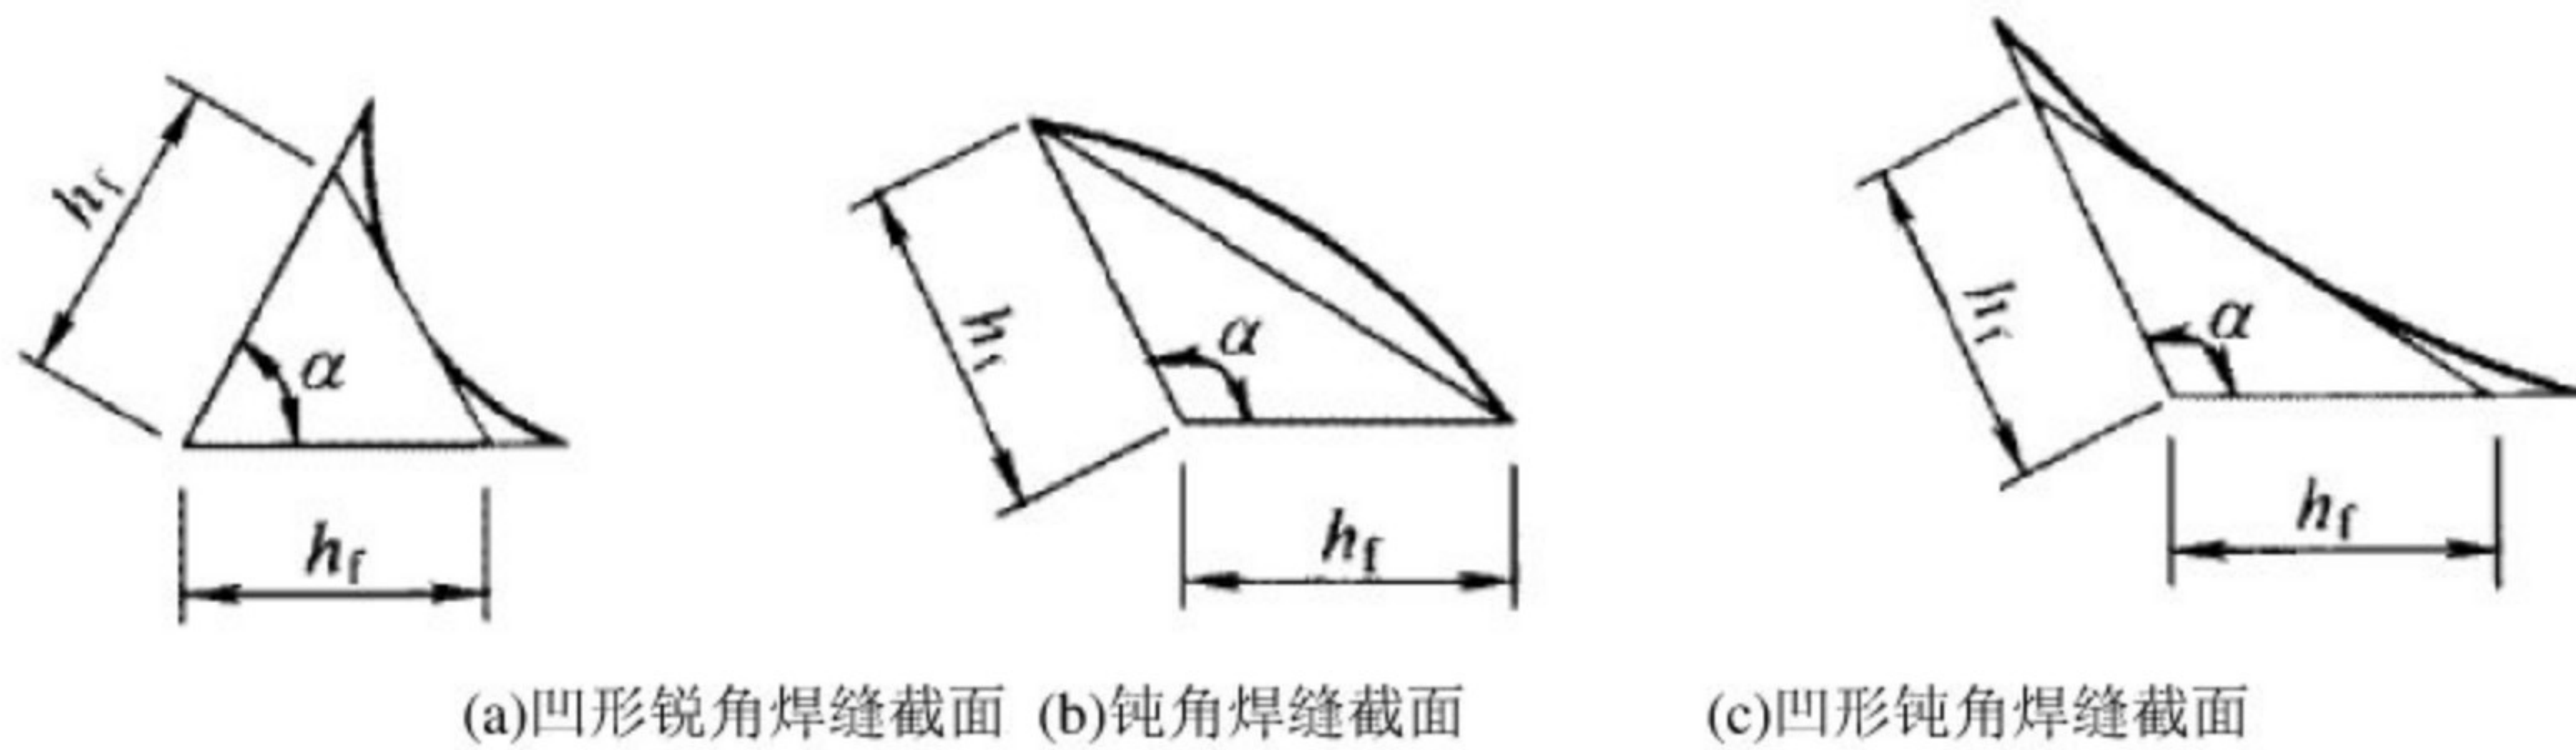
T 形连接的斜角角焊缝截面
